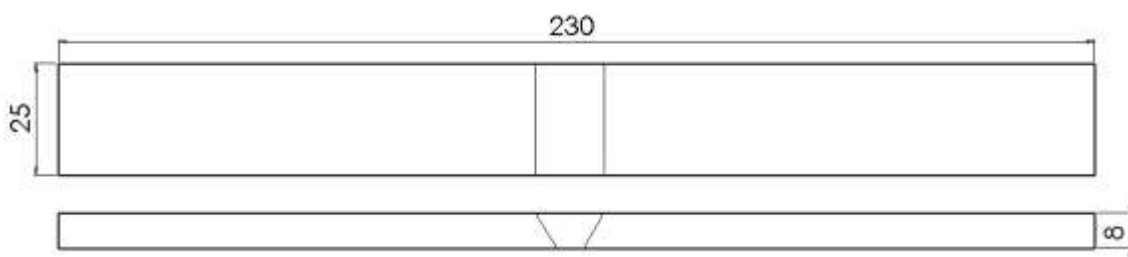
Dimensiones, probeta de ensayo de doblado.
